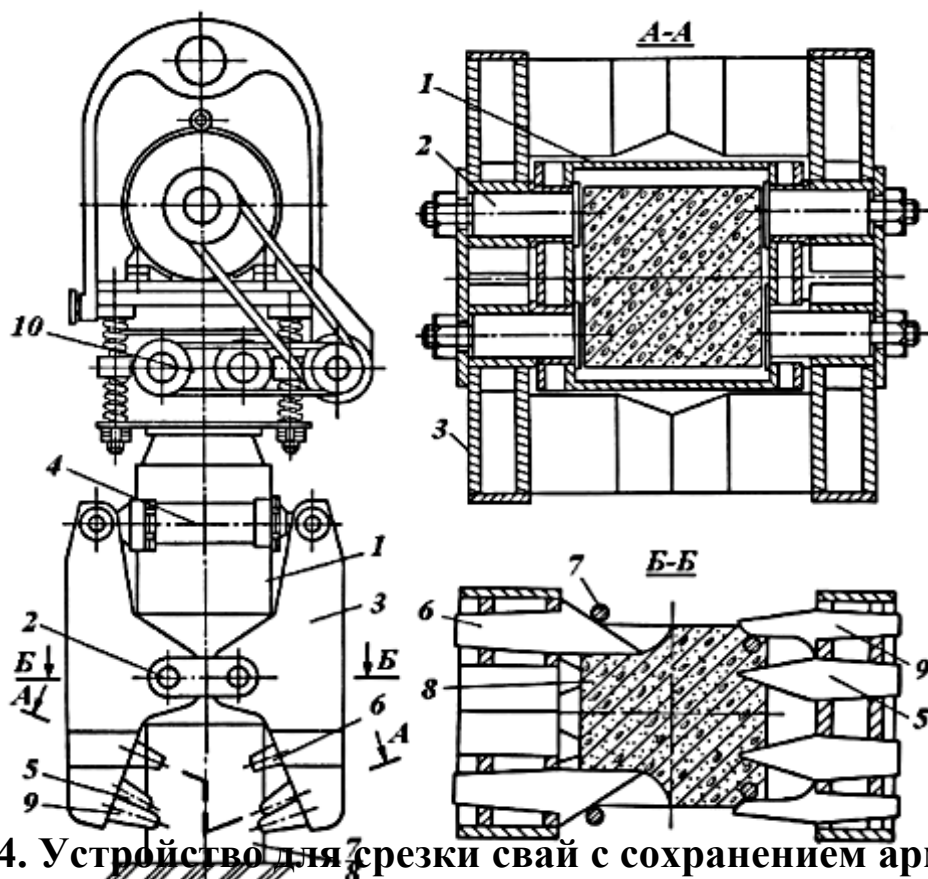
Устройство для срезки свай с сохранением арматуры над срезом.
